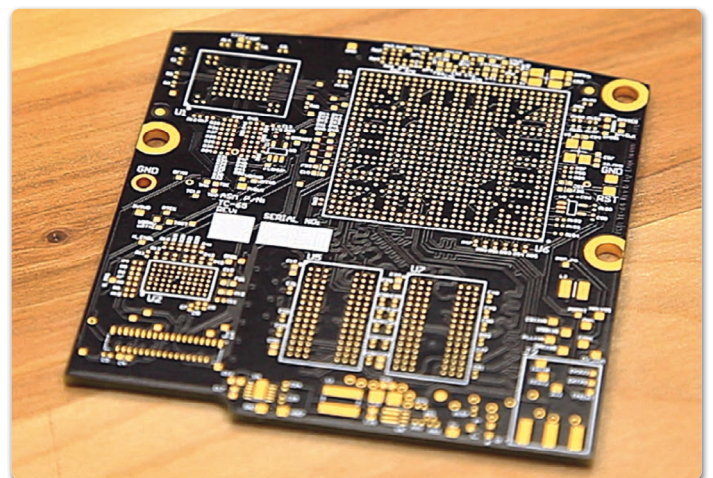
Das Routing eines großen BGA kann viel Zeit in Anspruch nehmen; Software-Werkzeuge für das PCB Layout, die ein automatisiertes BGA Breakout bieten, können den Zeitaufwand von Tagen auf Minuten reduzieren © Engenious Designs
